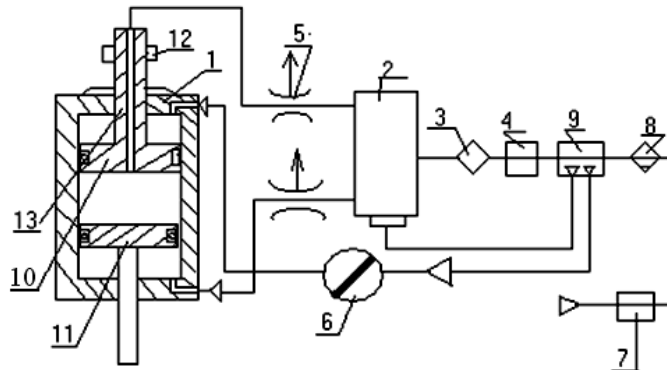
Пневматична схема машини точкового зварювання типу МТ
